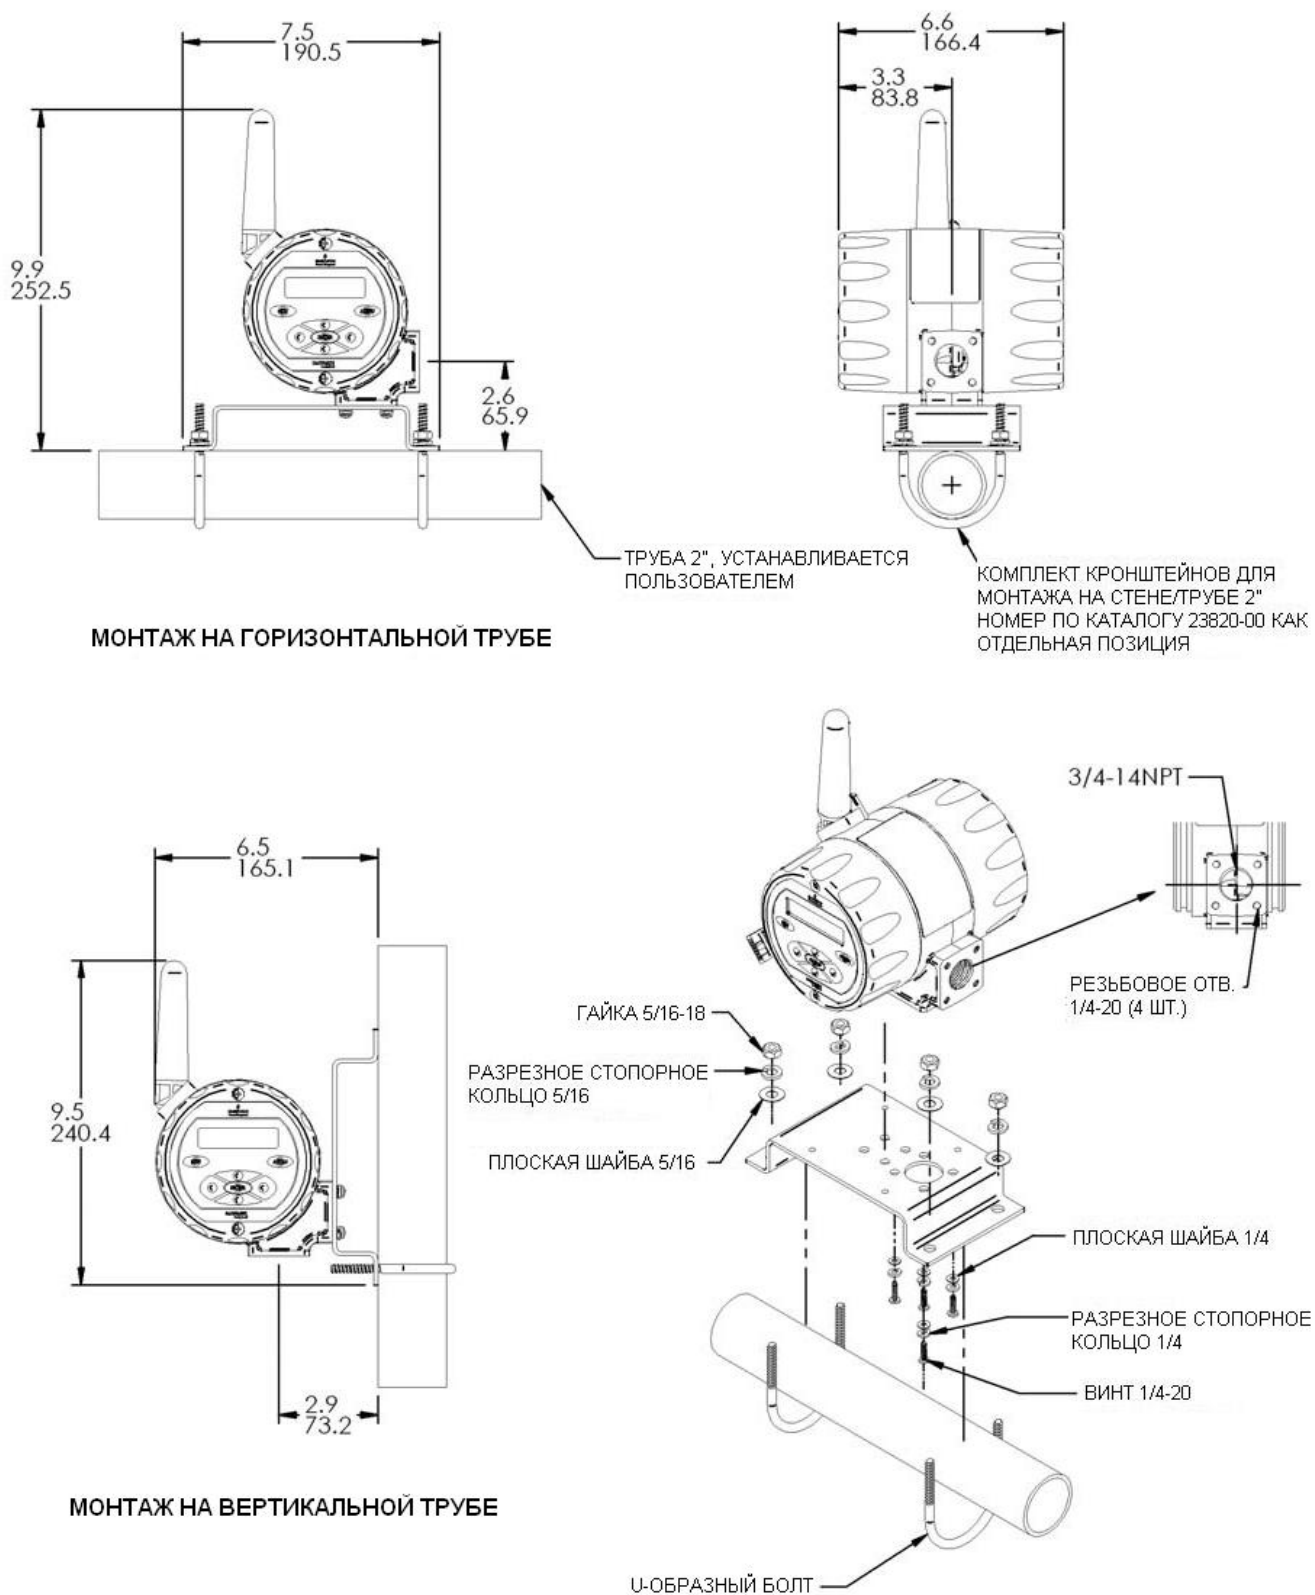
Установка датчика модели 6081 на трубопроводе. Используйте комплект монтажного кронштейна для установки на трубопроводе/стене, номер по каталогу 23820-00
